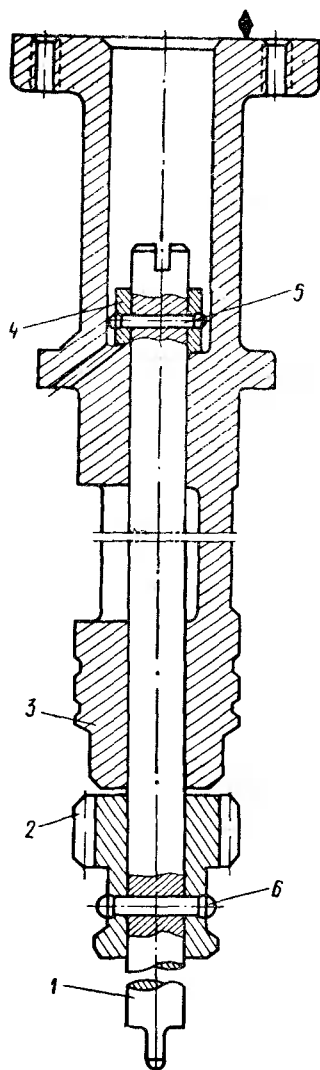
Привод прерывателя-распределителя двигателя ЗИЛ-130:
